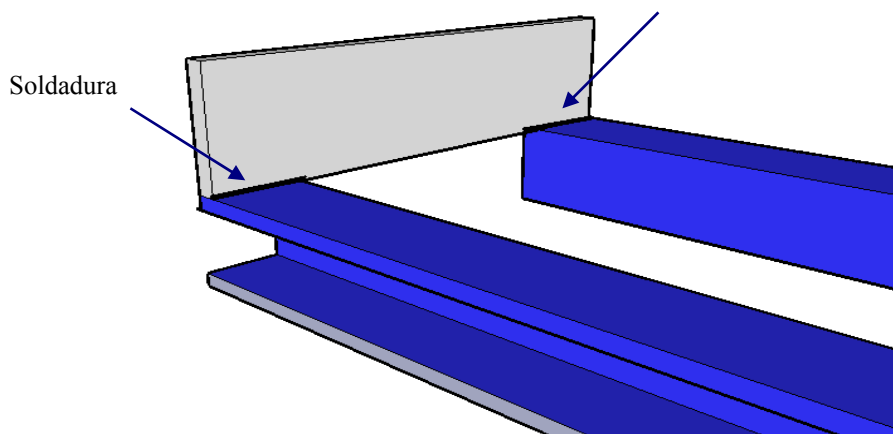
Soldadura entre la lámina y el perfil. Fuente Propia.
